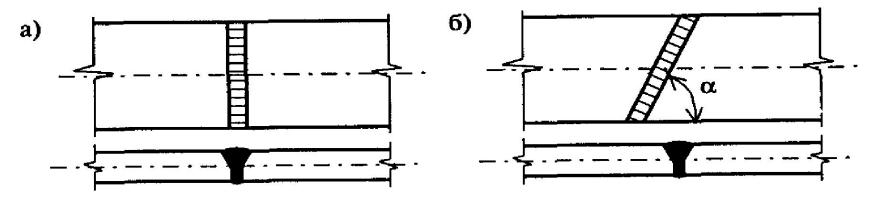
Стыковые сварные соединения: а) прямой стыковой шов; б) косой стыковой шов, α = 45-60°
